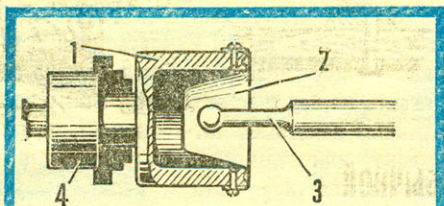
Схема обработки листового материала методом выдавливания: 1 — матрица (твердое дерево или металл), 2 — металлическая пластина, 3 — давилник, 4 — патрон токарного станка.
